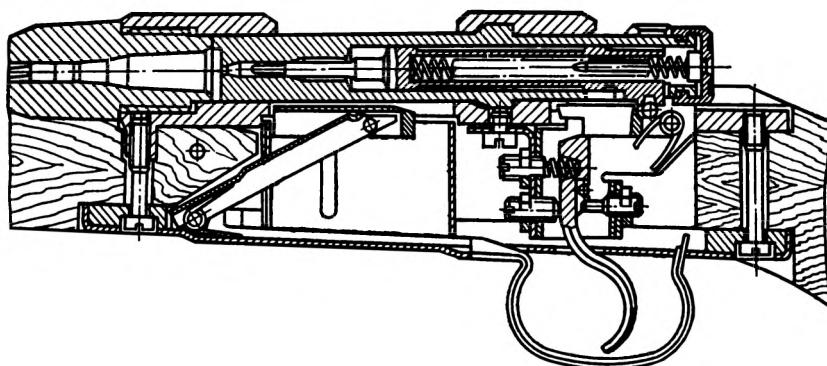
Схема устройства ударно-спускового, запирающего и подающего механизмов карабина «Барс»
